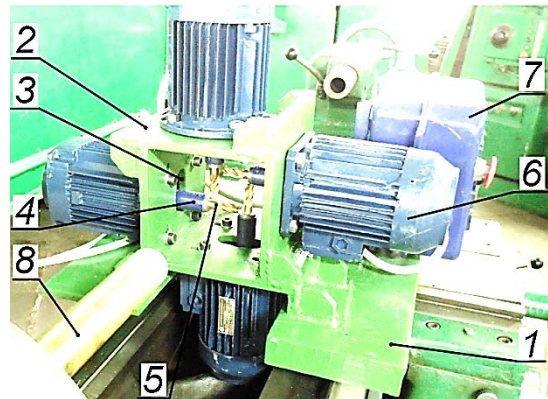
Супорт токарного верстата: 1 – кріпильна плита, 2 – корпус, 3 – наскрізні пази, 4 – цангові патрони, 5 – кінцеві фрези, 6 – електродвигуни, 7 – пульт керування; 8 – заготовка із склопластику [6]
